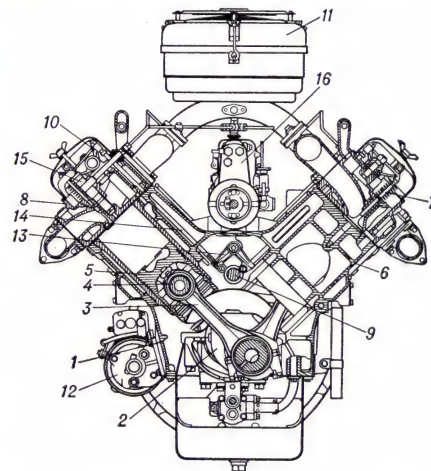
Поперечный разрез четырёхтактного дизеля ЯМЗ-236: позиции 1—10 и 12 — такие же, как на рис. 1; 11 — воздухоочиститель; 13 — толкатель; 14 — штанга; 15 — форсунка; 16 — насос высокого давления.
